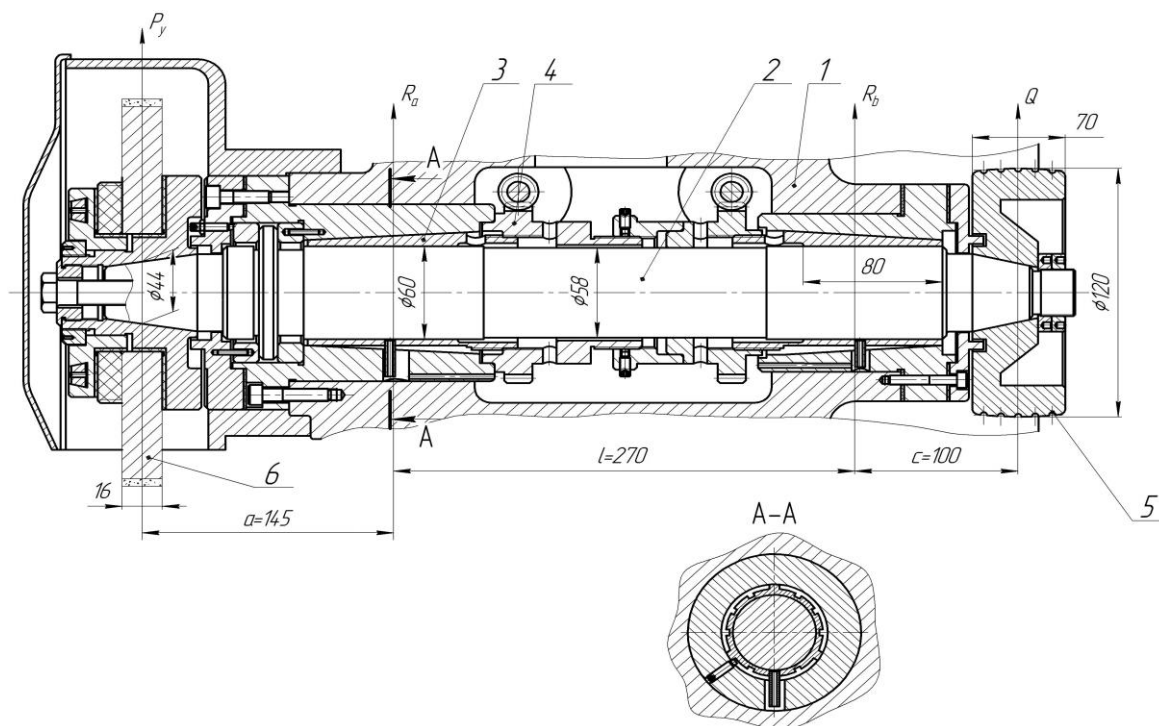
Шпиндельный узел плоскошлифовального станка мод. 3Г71 [4]: 1 – корпус; 2 – шпиндель; 3 – упруго-деформируемые втулки, образующие несущие карманы для смазки; 4 – механизм регулировки диаметрального зазора подшипников; 5 – приводной шкив плоскокоренной передачи; 6 – шлифовальный круг.
